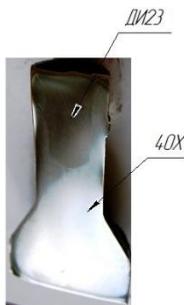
Фото продольного шлифа биметаллической детали типа «Выталкиватель»
